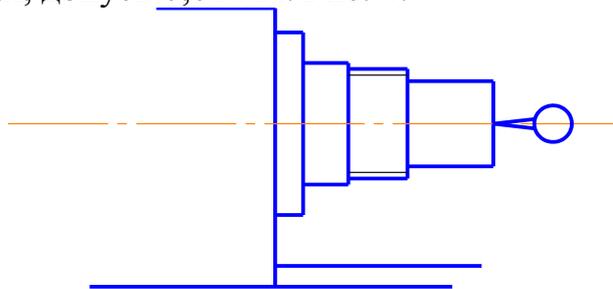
Схема установки индикатора для проверки осевого биения шпинделя
